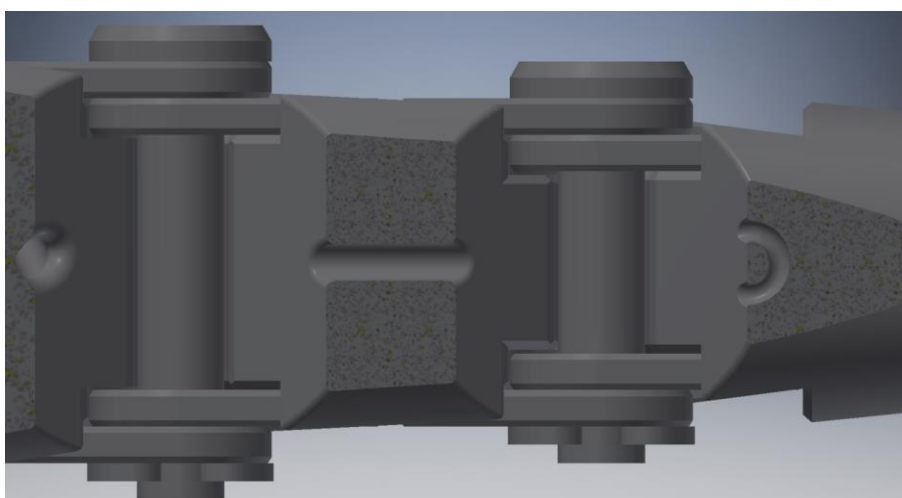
Prótese final - Detalhe rota de cabo tracionador
